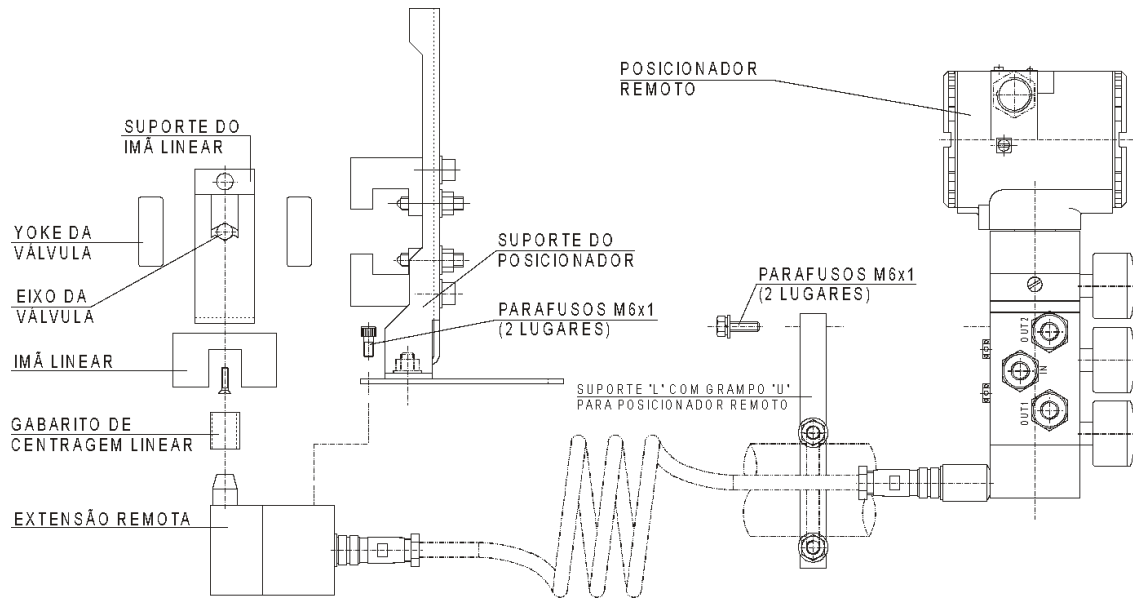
Posicionador em Atuador Linear com Sensor de Posição Remoto
